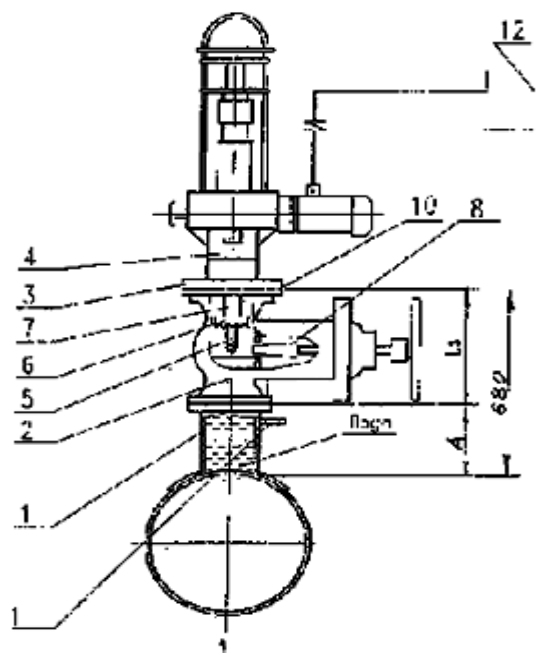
Монтажная схема вырезки отверстия в трубопроводе
